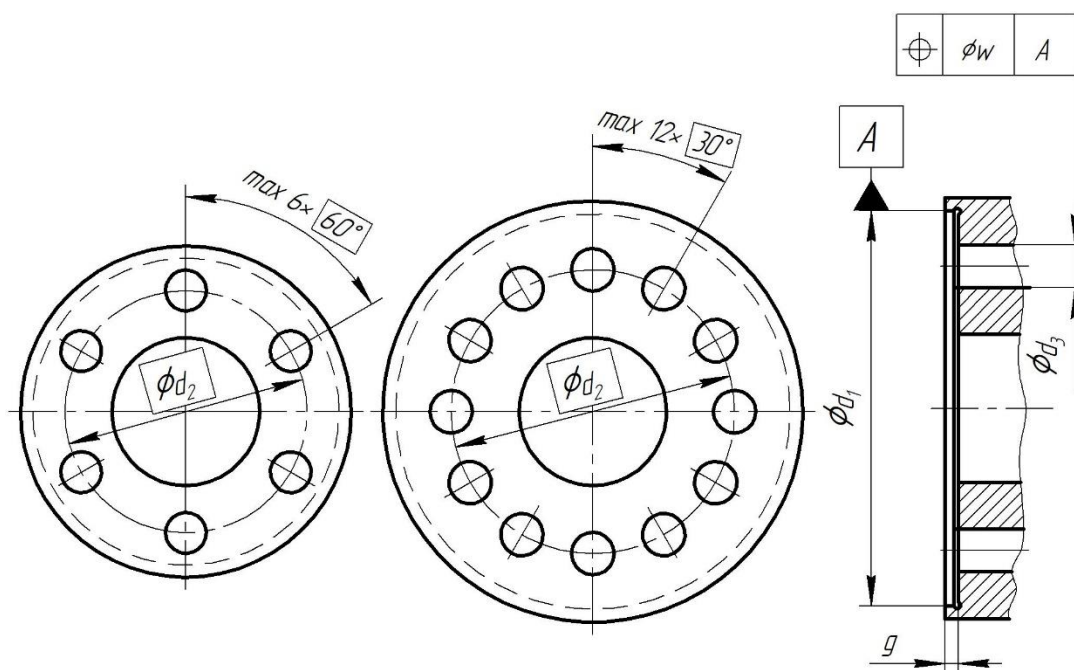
Присоединительные поверхности рабочих зажимных устройств
